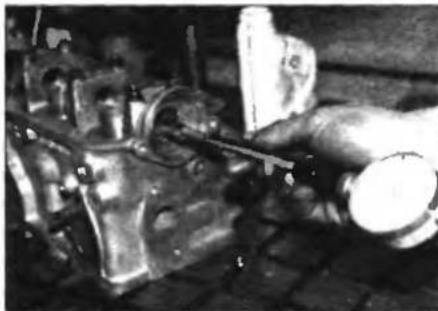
Измерение диаметра постелей распределительного вала в головке блока
